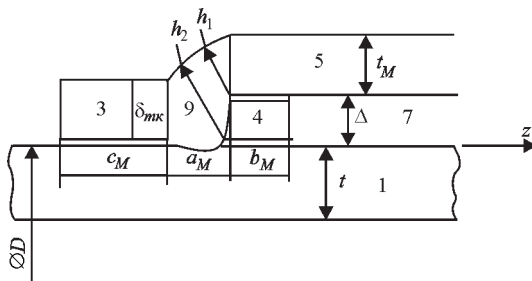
Схема перерізу кільцевого з'єднання монтажного вузла кріплення герметичної муфти з компаундним наповнювачем до трубопроводу
